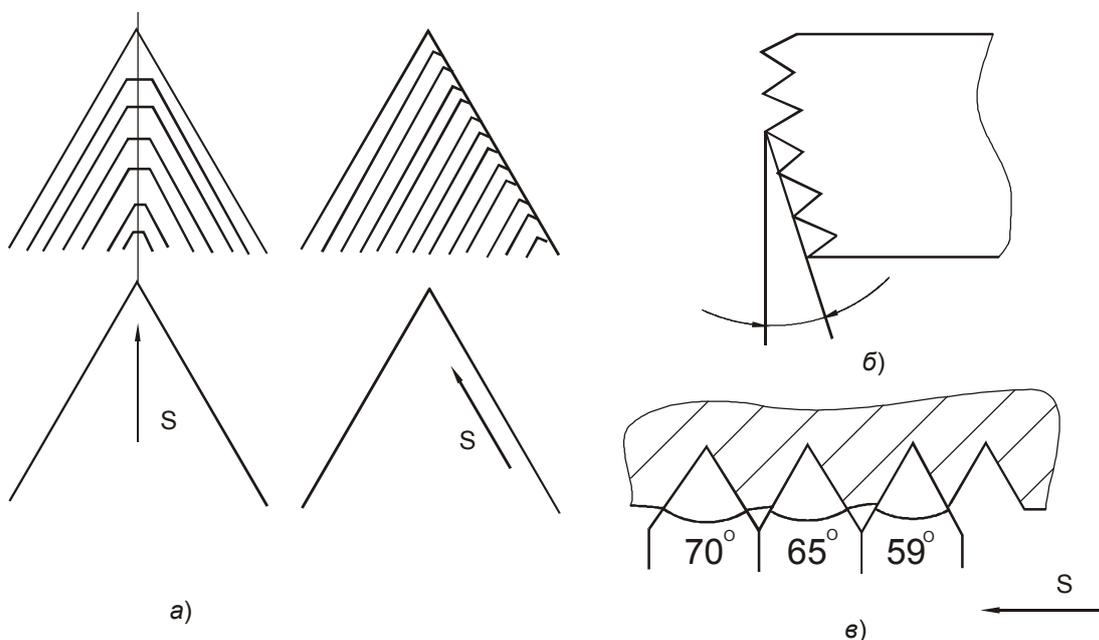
Схемы нарезания резьбы: а – с радиальной подачей и с подачей вдоль одной из сторон; б – расположение зубьев резьбовой гребенки; в – набором резцов
